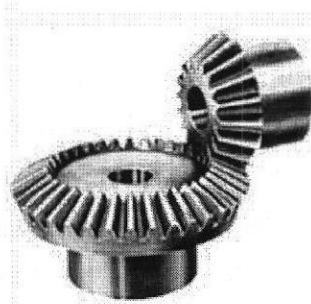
Montagem de parte de um diferencial, utilizando engrenagens cônicas de dentes retos (Nice, 2010)
